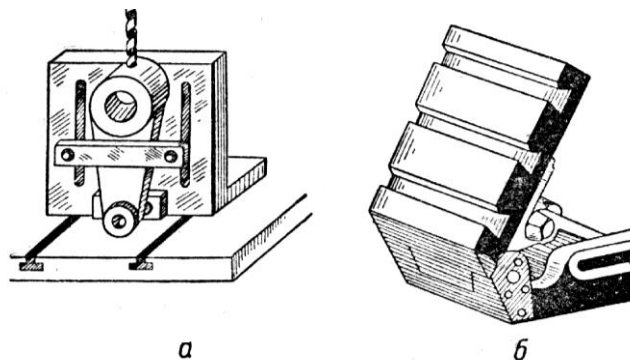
Косинці для закріплення деталей складної форми: а — звичайний; б — універсальний
